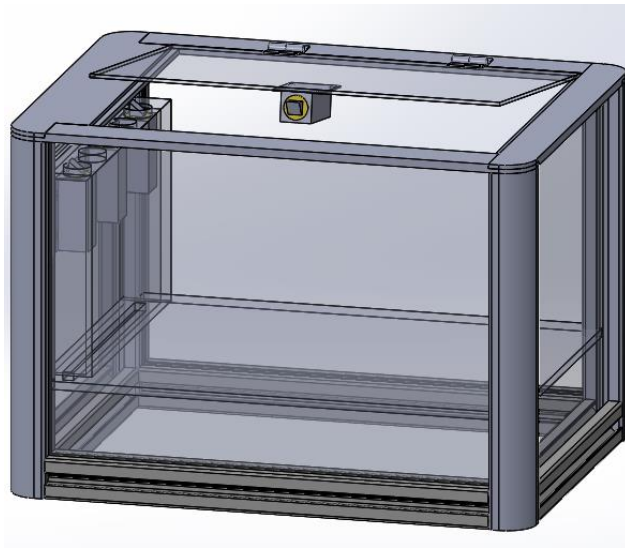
Diseño general del contenedor de tarjetas PCB no conformes
